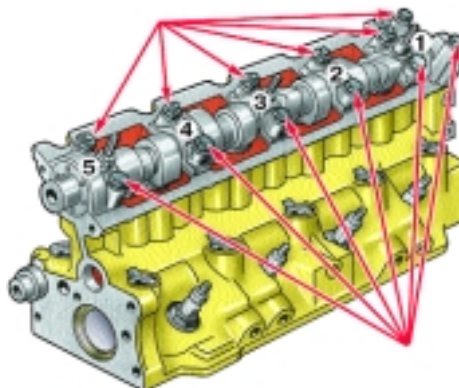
Крепление крышек подшипников распределительного вала двигателя F3R 272
